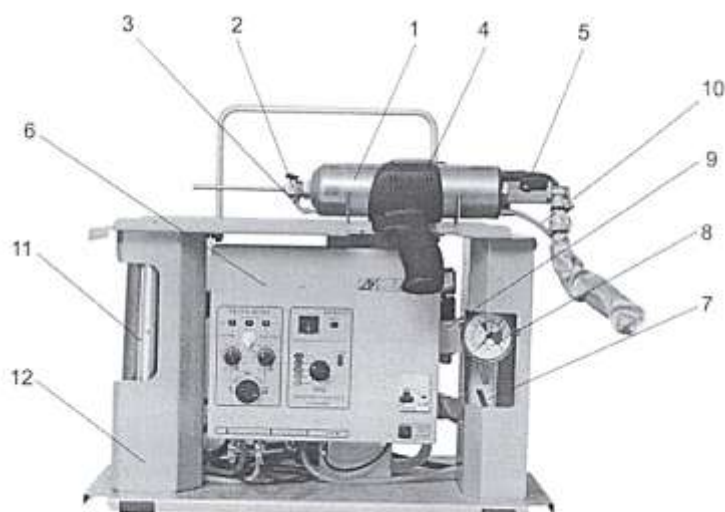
Установка для газодинамического напыления покрытий ДИМЕТ (404)
